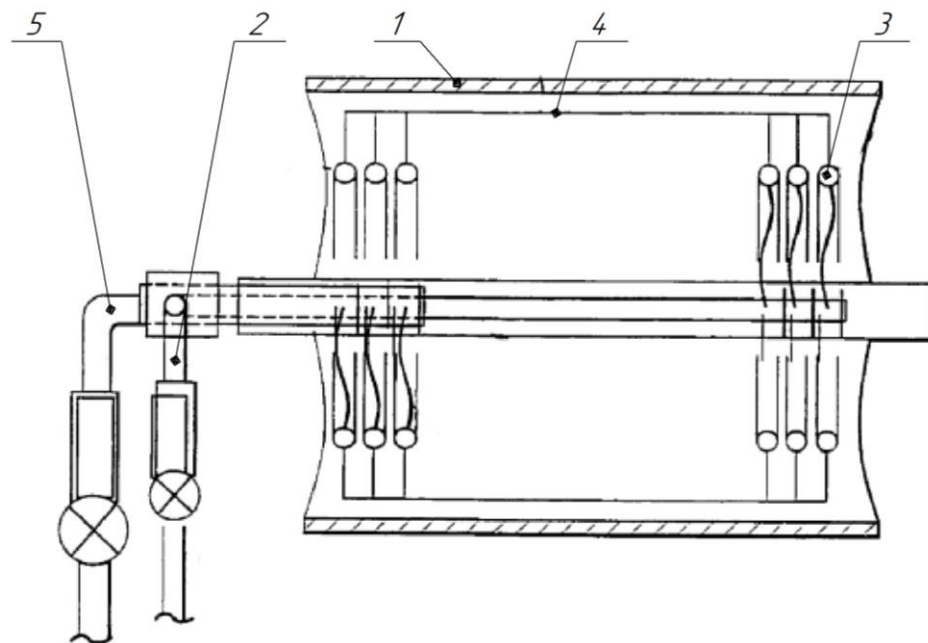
Пристрій для обробки волокнистого полотна
